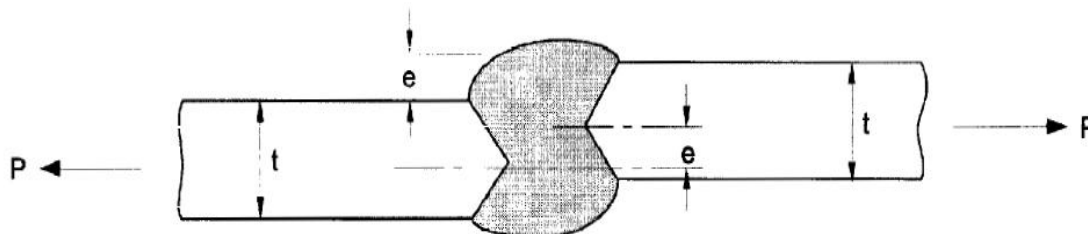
Desalineamiento circunferencial de una tubería soldada tipo bisel.
